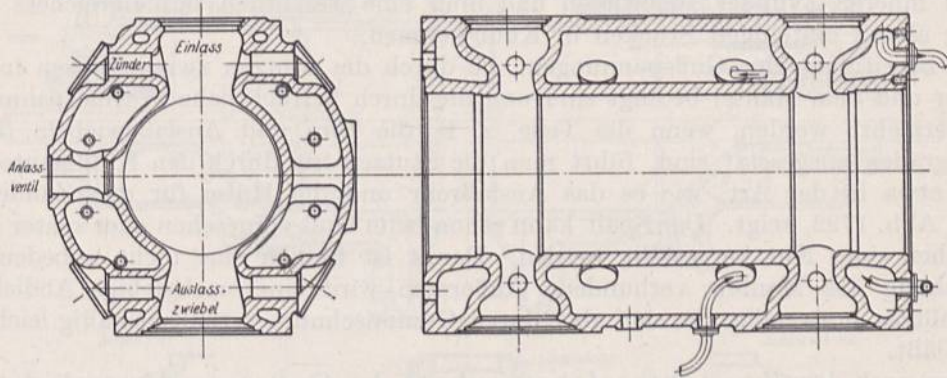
Viertaktgroßmaschinenzylinder, Ausführung der Maschinenfabrik Augsburg—Nürnberg.
